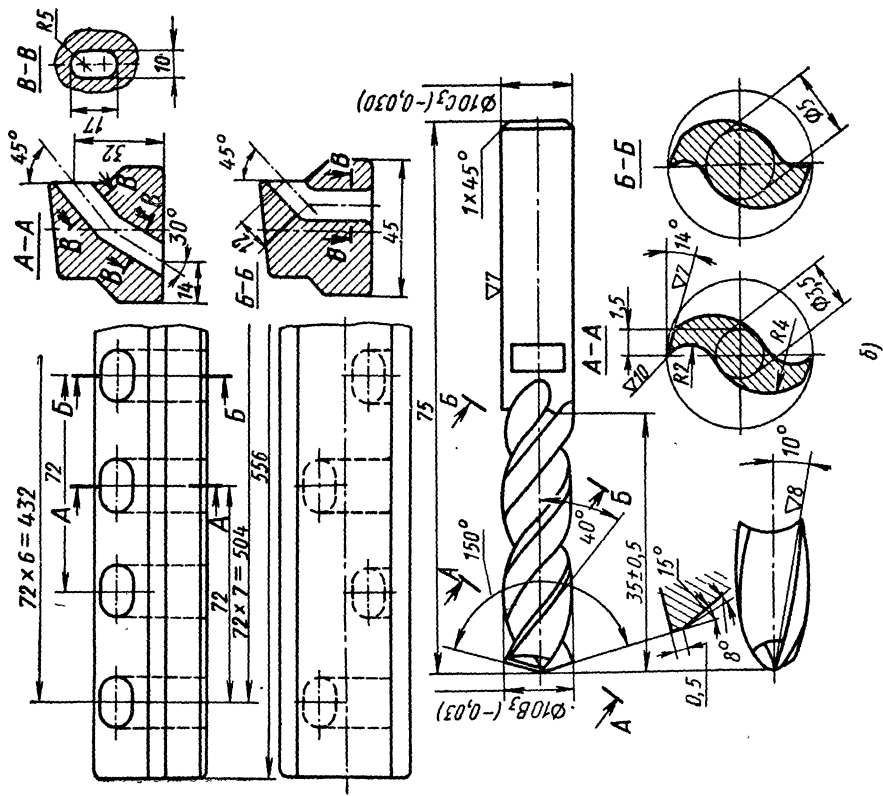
Быстротермостойкое приспособление для сверлильно-фрезерной операции
